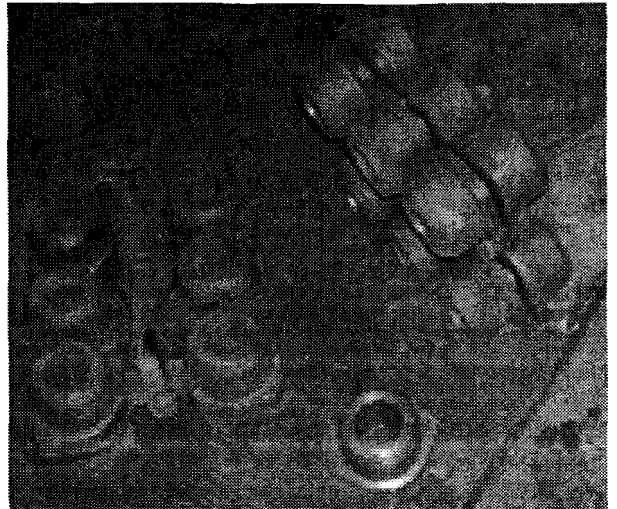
Куст отливок «Втулка», изготовленный литьем в оболочковые формы, и деталь после механической обработки
